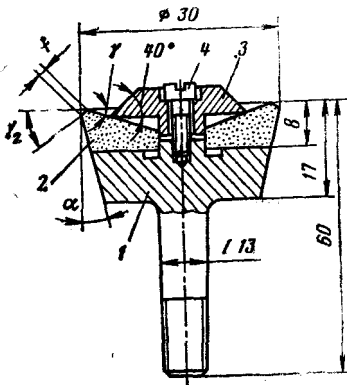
Чашечный твердосплавный резец со стружколомающим устройством для обточки восстанавливаемых бандажей колесных пар: 1 — корпус; 2 — режущая пластина; 3 — стружколомающая пластина; 4 — винт
